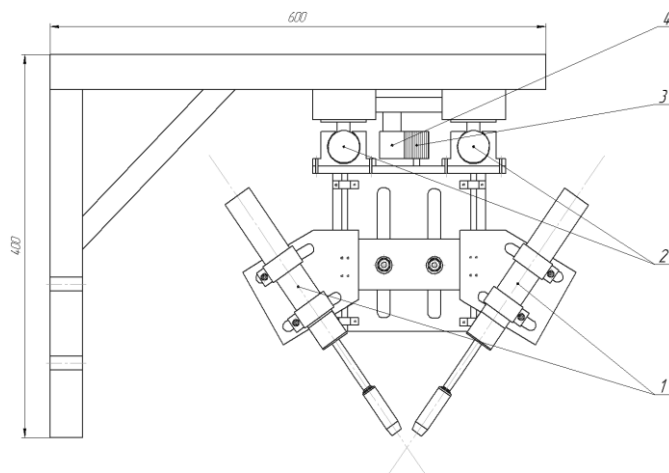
Схема установки для автоматической двухдуговой наплавки
